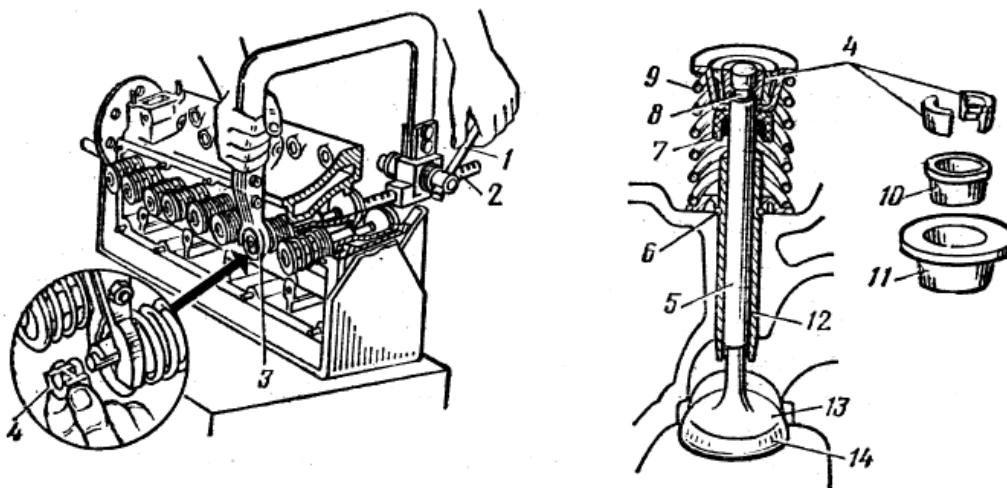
Устройство клапана двигателя ЗМЗ-53:
